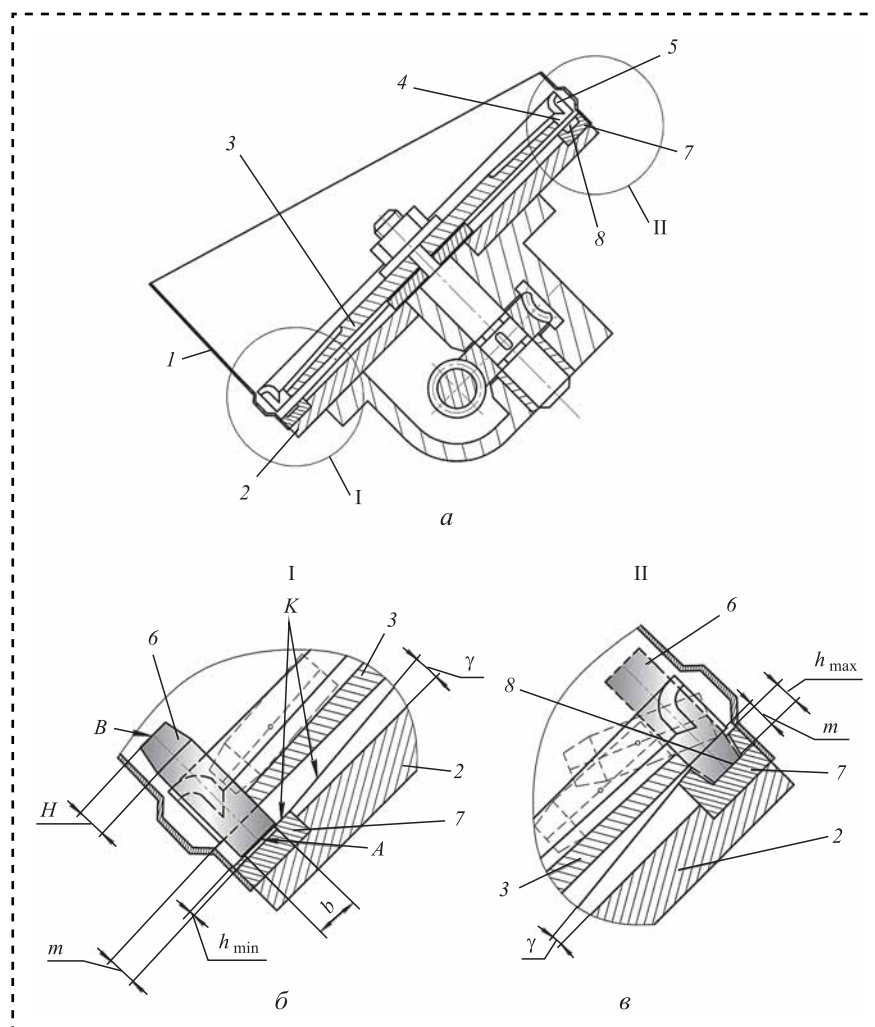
Усовершенствованная конструкция зубчатого бункерного загрузочного устройства с кольцевым ориентатором:
